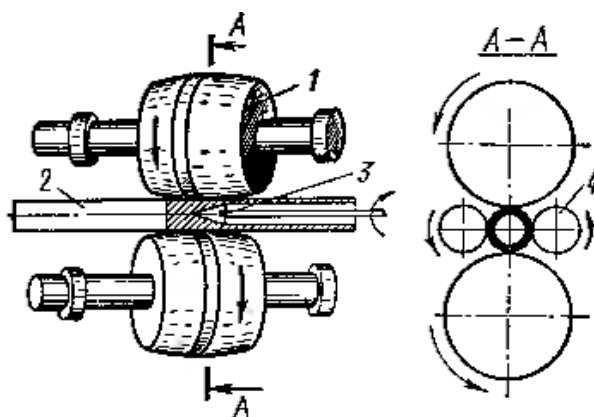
Схема прошивного стана с бочкообразными валками
